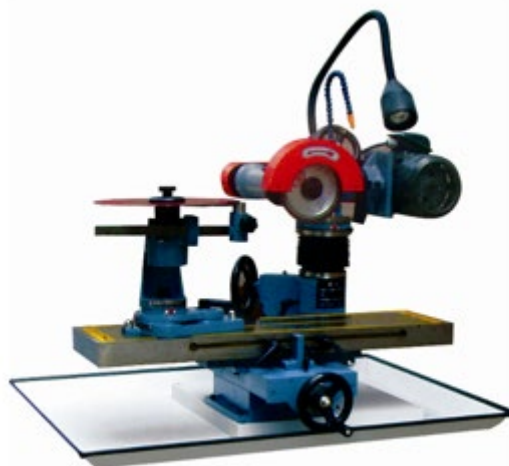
Заточка дисковых пил с твердосплавными зубьями
